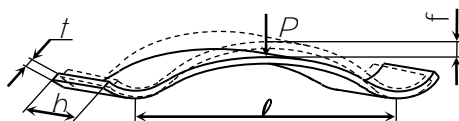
Внешний вид плоской пружины с основными конструктивными параметрами
